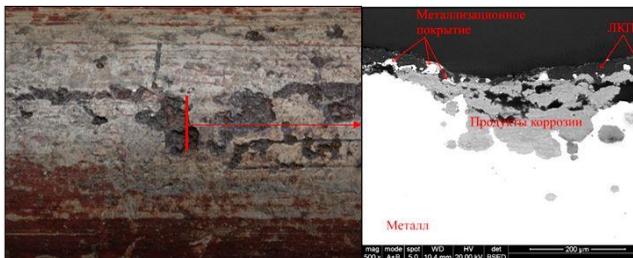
Повреждения (абразивный износ) корпуса ПЭД. Образец №3
